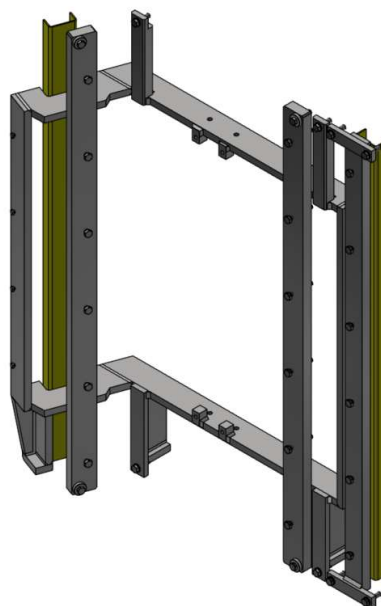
Referência do conjunto da estrutura da Guilhotina.
